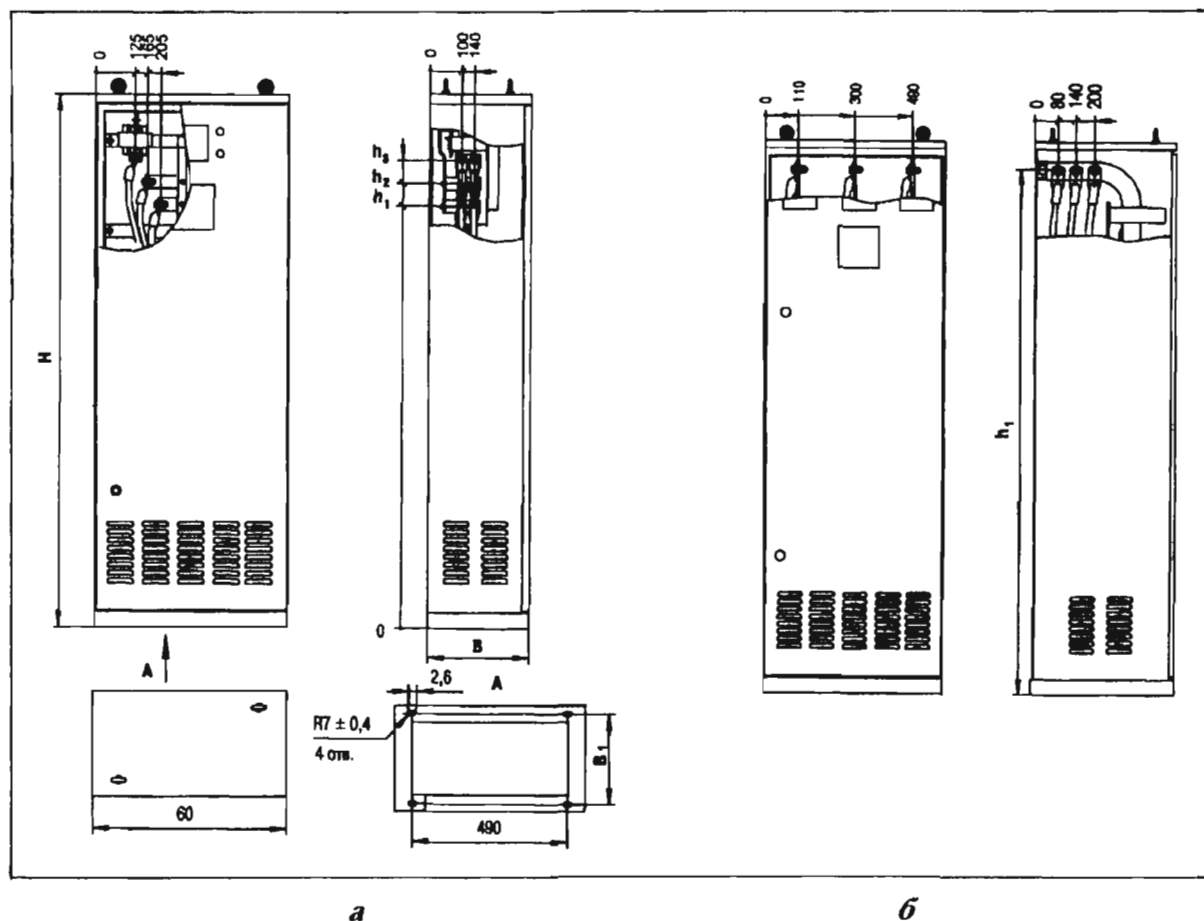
Габаритные размеры конденсаторных установок типа УКМ63-0,4
